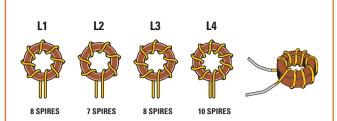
Fabrication des selfs toroïdales (le nombre de spires à bobiner sur le noyau toroïdal est indiqué sous les dessins). N'oubliez pas, avant insertion et soudure, de racler l'émail des extrémités du fil et de les étamer sur environ dix millimètres
